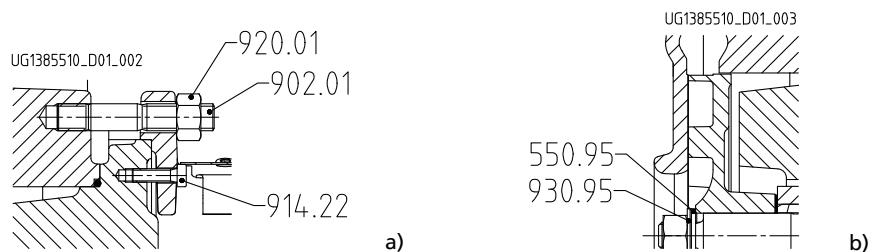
а) Зажимная крышка корпуса б) Крепление рабочего колеса при узле вала 25
